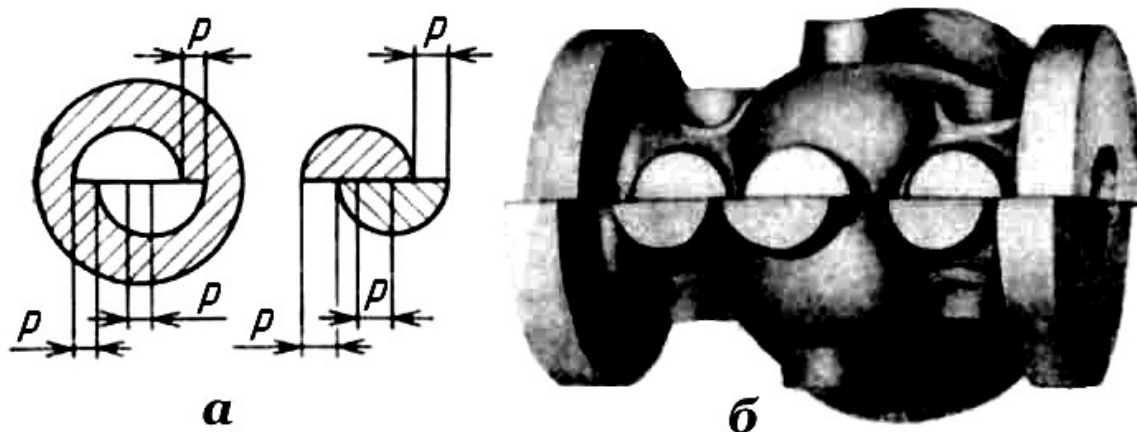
Перекос: а – схема; б – дефектная отливка
